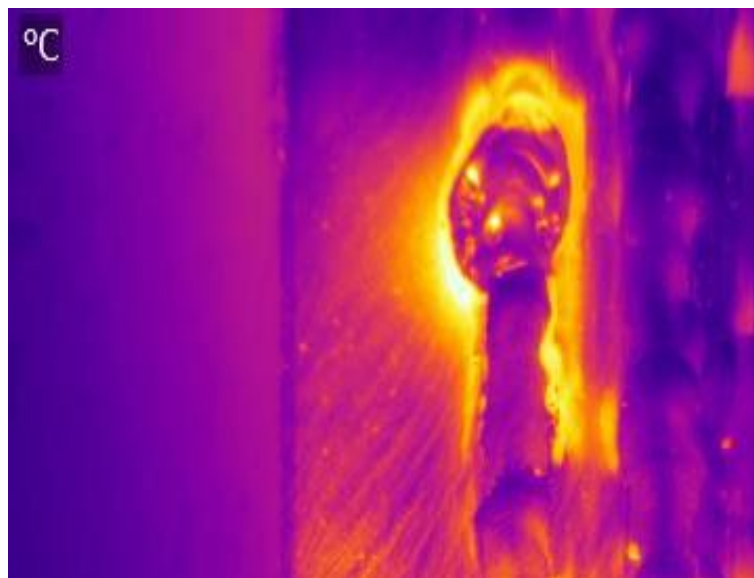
Cordón de soldadura afectado por porosidad (1).
